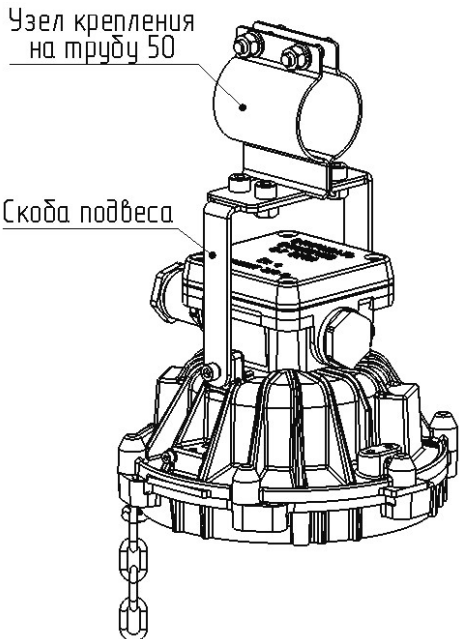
Светильник ДСП57КР-02, на узле крепления на трубу d=50мм.
